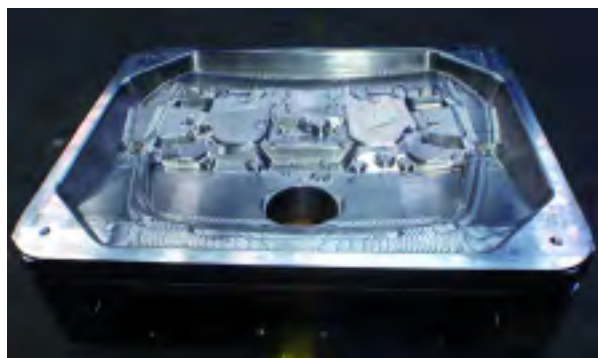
Inserto del molde para el marco de soporte de la puerta del maletero 1.350 mm x 1.720 mm x 440 mm, 5.440 kg.
